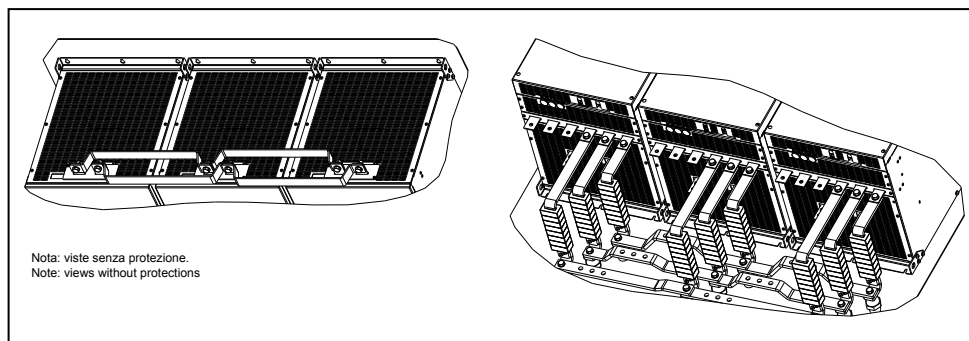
Набор шин для типоразмеров 900 - 1000 кВт
